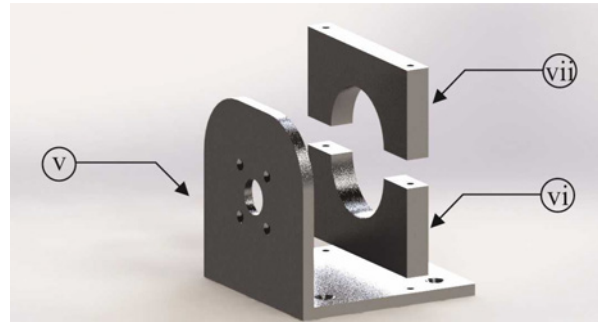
Vista explosionada de la base del motor dibujada en SolidWorks.
